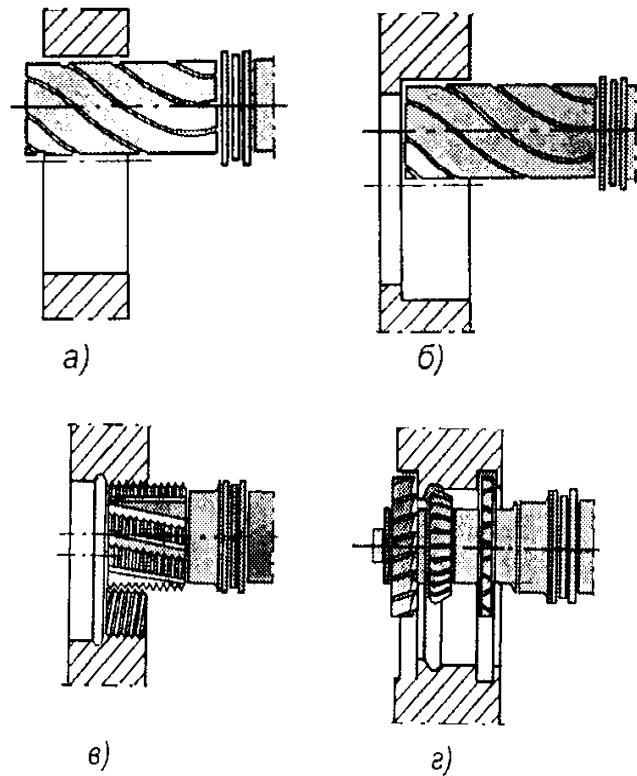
Схемы обработки отверстий на фрезерных станках
